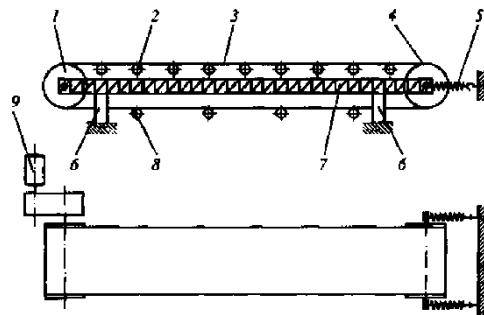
Ленточный конвейер: 1 - приводной барабан; 2 - роlikоопора грузовой ветви; 3 - конвейерная лента; 4 - натяжной барабан; 5 - натяжное устройство; 6 - опоры конвейера; 7 - рама конвейера; 8 - роlikоопора холостой ветви; 9 - привод конвейера
